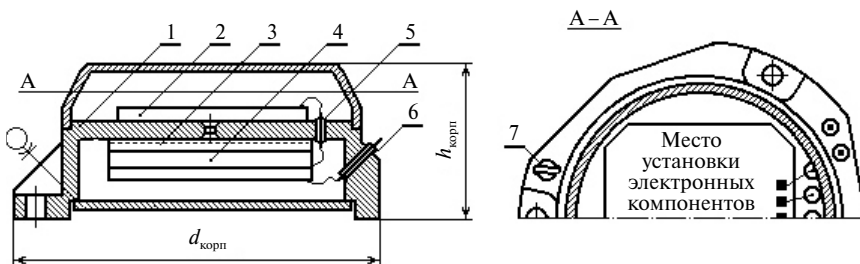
Корпус акселерометра с цилиндрическими отсеками: 1 — основание; 2 — электронная плата; 3 — стеклянный слой; 4 — ЧЭ; 5, 6 — проходные изоляторы; 7 — трубка для заполнения
